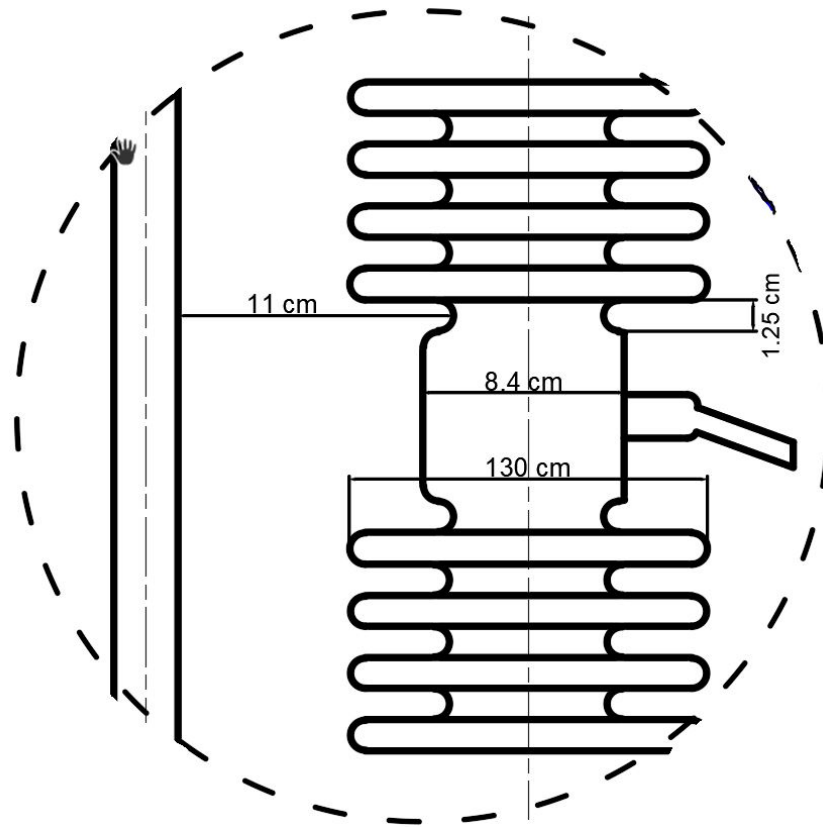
Partes de un seccionador (Enersis, 2012)
